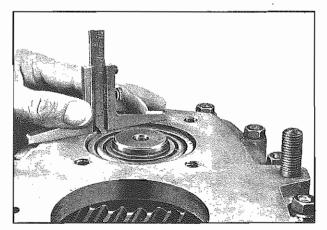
Misurazione del gioco tra l'anello esterno del cuscinetto e la parte frontale della scatola - Measuring gap between bearing outer race and face end of housing
